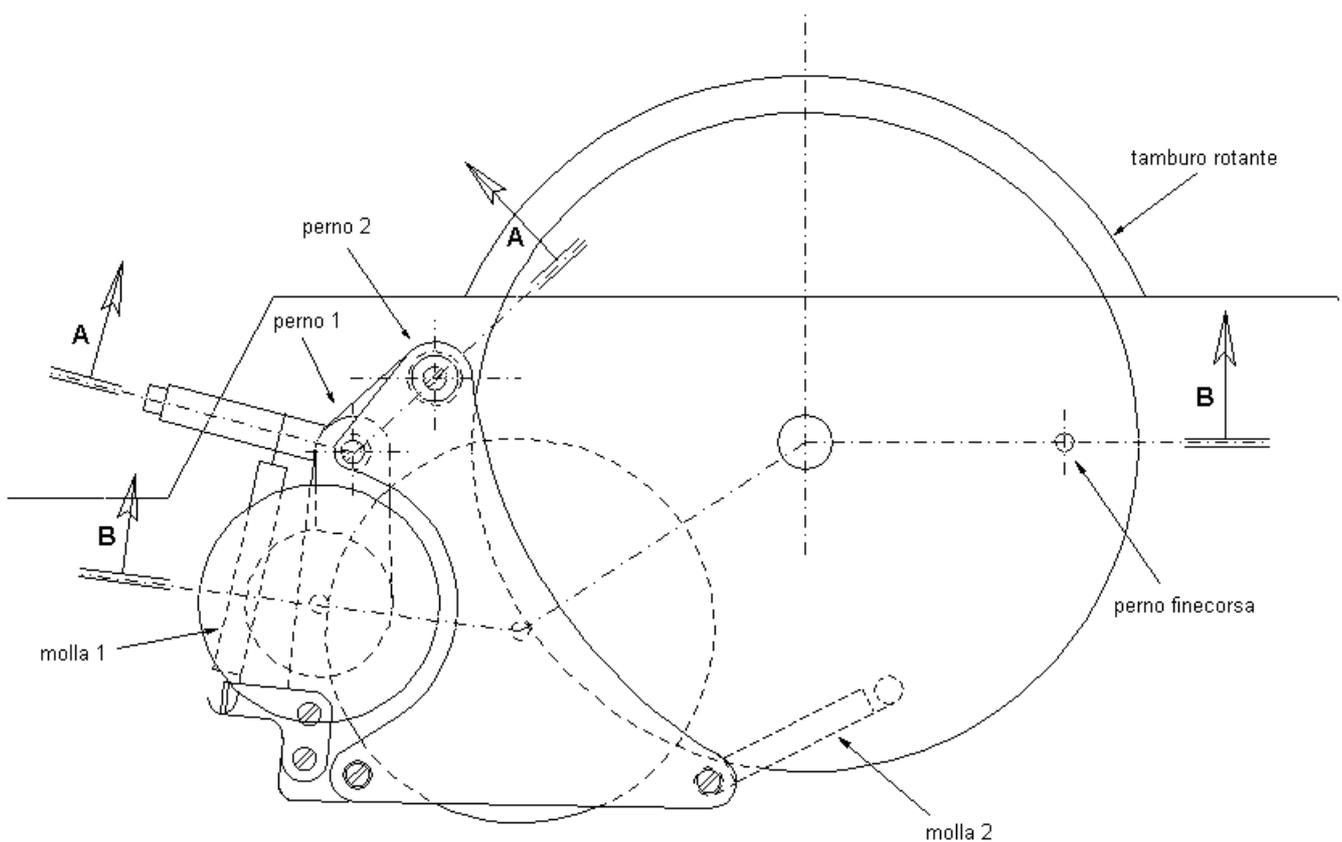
Pianta del dispositivo di rotazione dell'obiettivo (schema).
